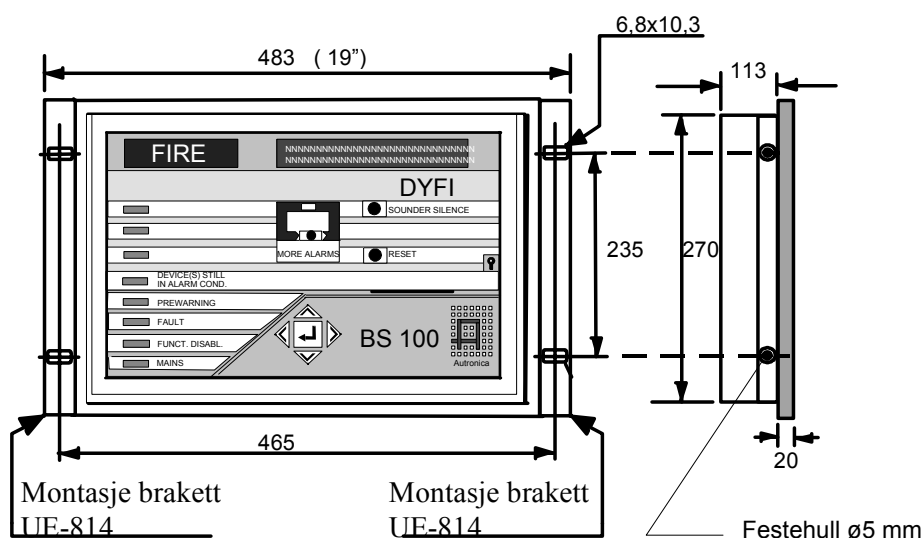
Dimensjoner (inkl. montasjebrakett) ved montasje i 19" rack.
